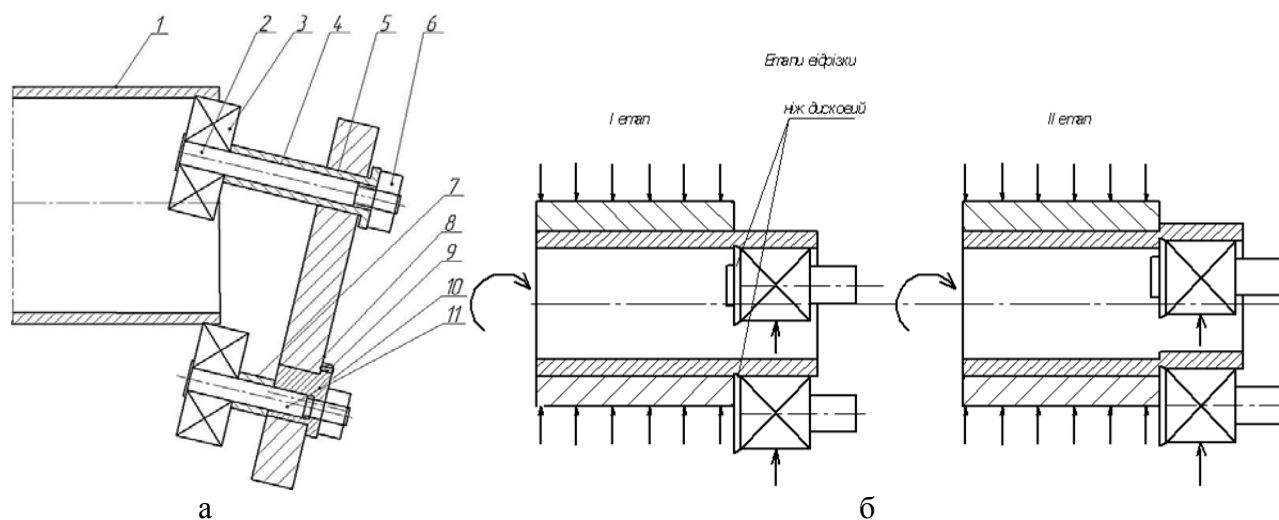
Устройство для отрезки трубчатых заготовок от цилиндрической трубы [7]
